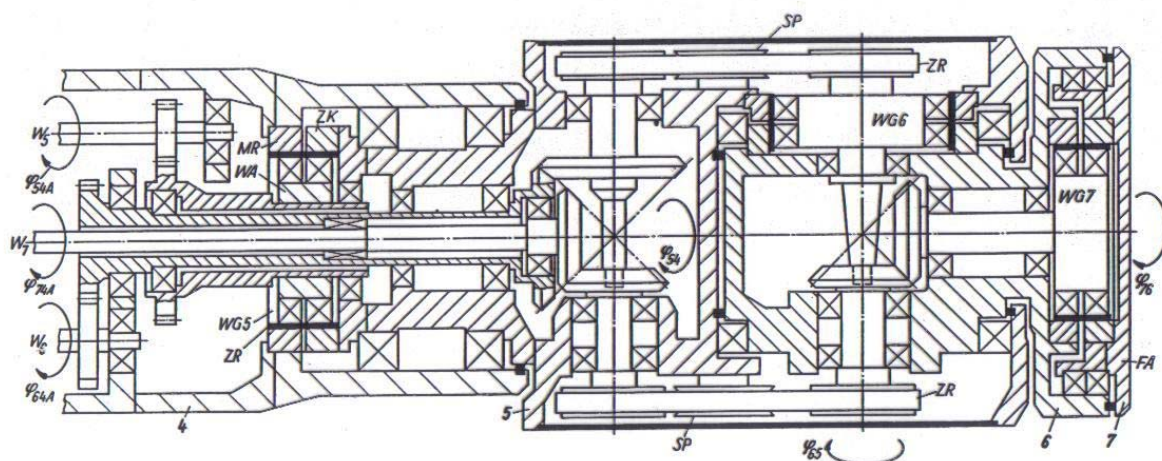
2 Konstrukce 2 DOF OÚ
